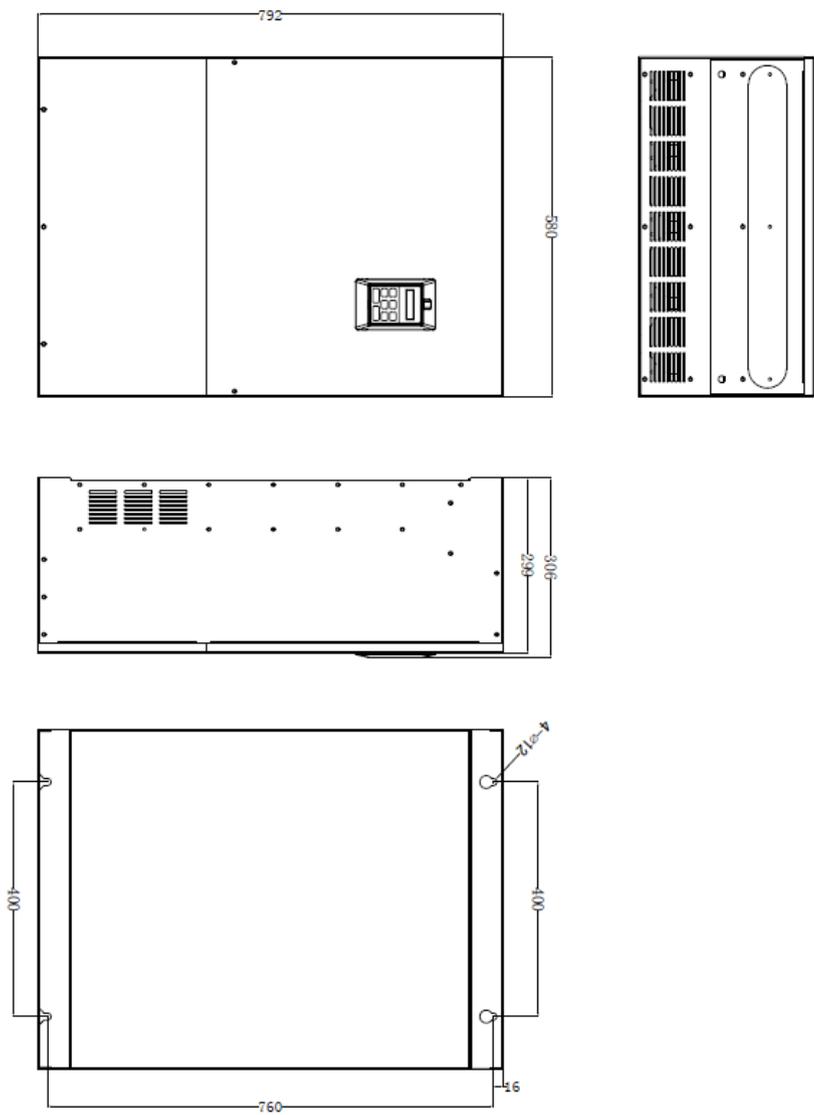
132-160KW 外型尺寸及安装尺寸示意图
